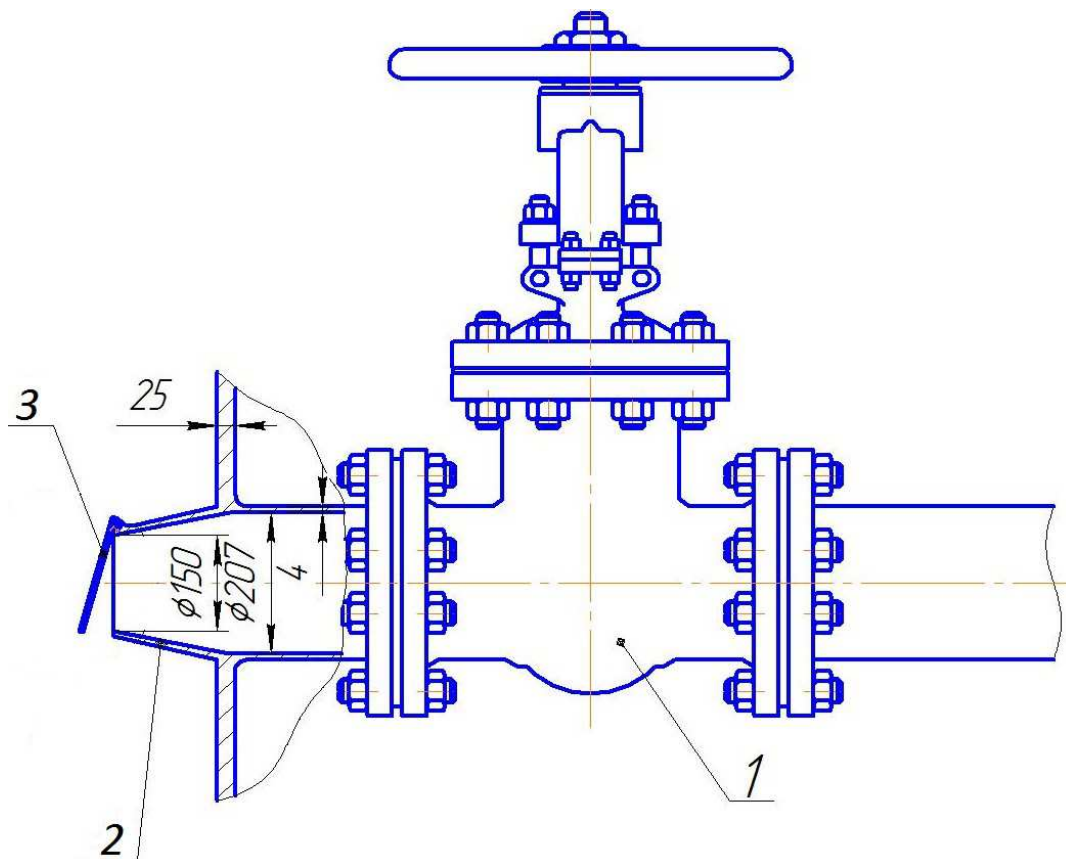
Устройство напорного патрубка напорно-размывной линии
